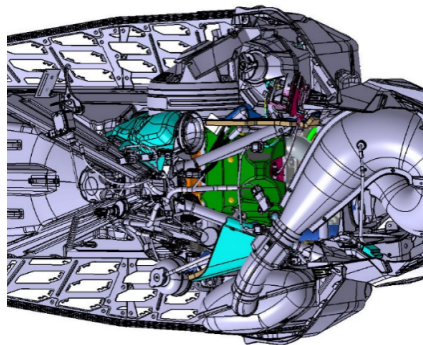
Emplacement des pièces dans le compartiment moteur de la motoneige (vue du haut)
